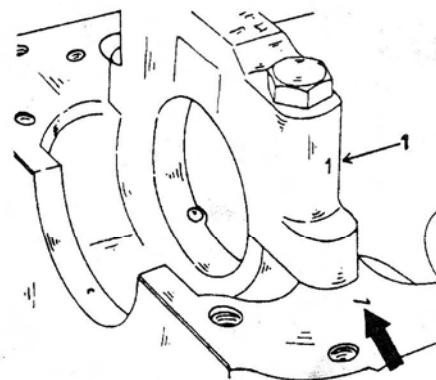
Маркировки крышки коренного подшипника находятся в указанных местах (1).
